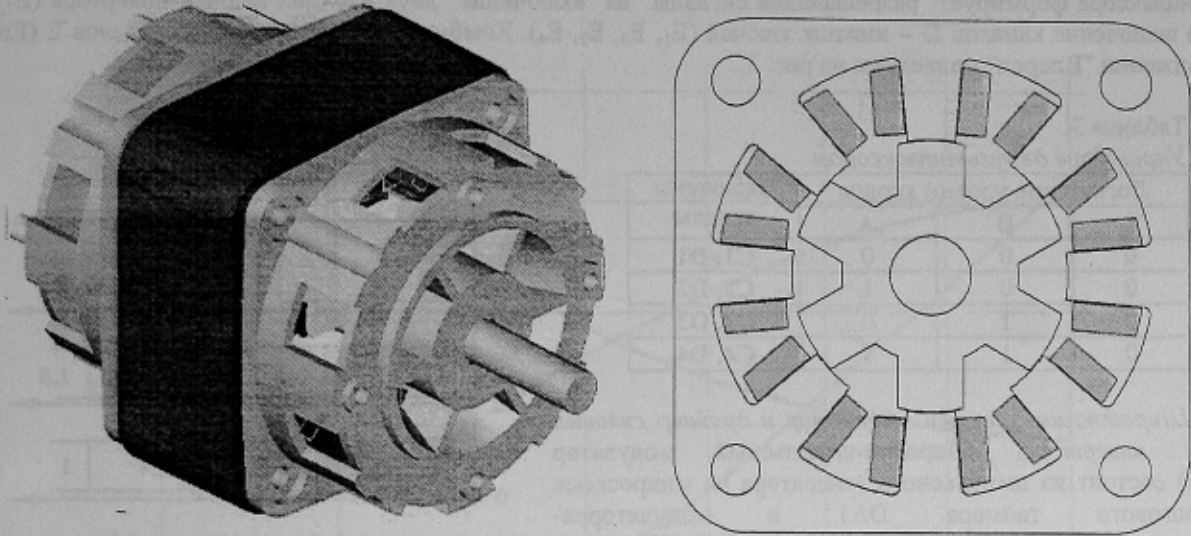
Внешний вид двигателя и его поперечный разрез
